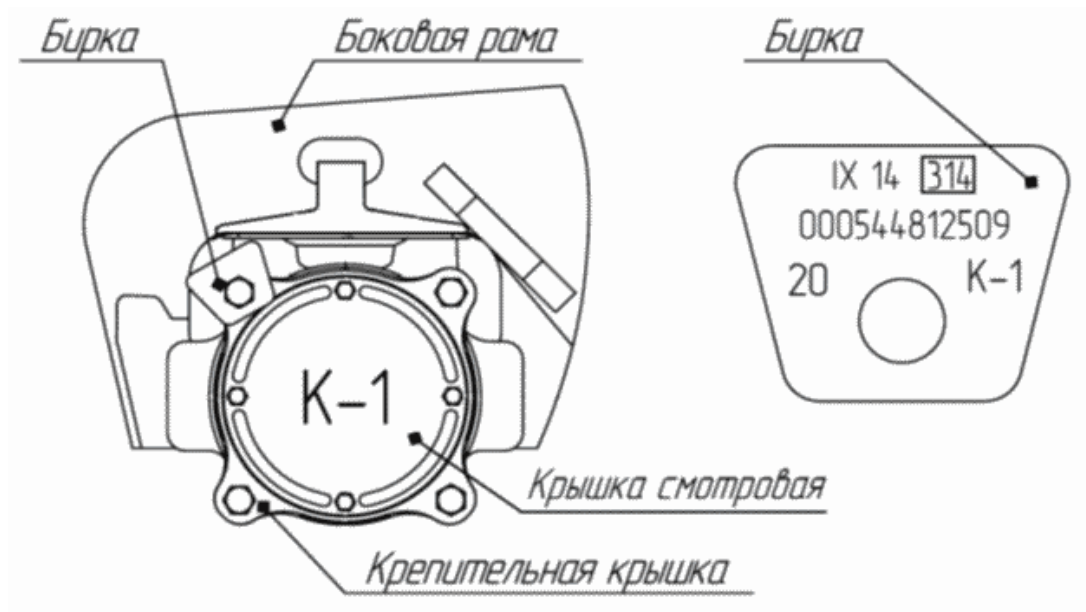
Внешние отличительные признаки буксовых узлов с подшипниками кассетного типа в габаритных размерах 130x250x160 мм торговой марки «BRENCO»
